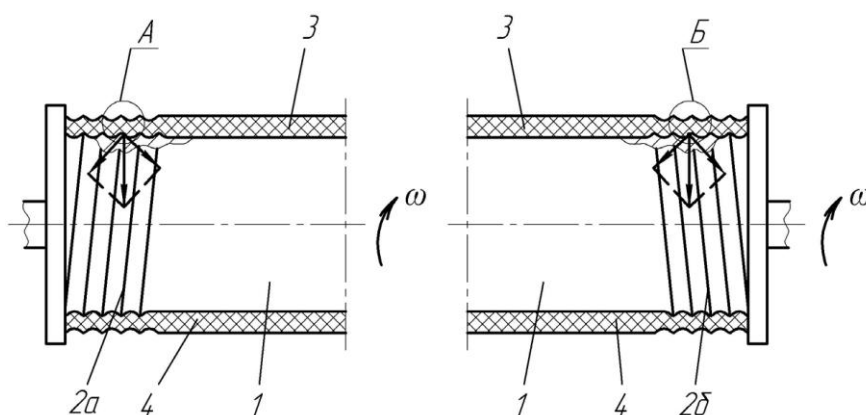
Розрізи привідного барабана: 1 – середня частина; 2а, 2б – нарізні частини; 3, – набігаючі та збігаючі гілки стрічки; 4 – збігаюча гілка стрічки; 5 – підшипники; 6 – вал барабана
